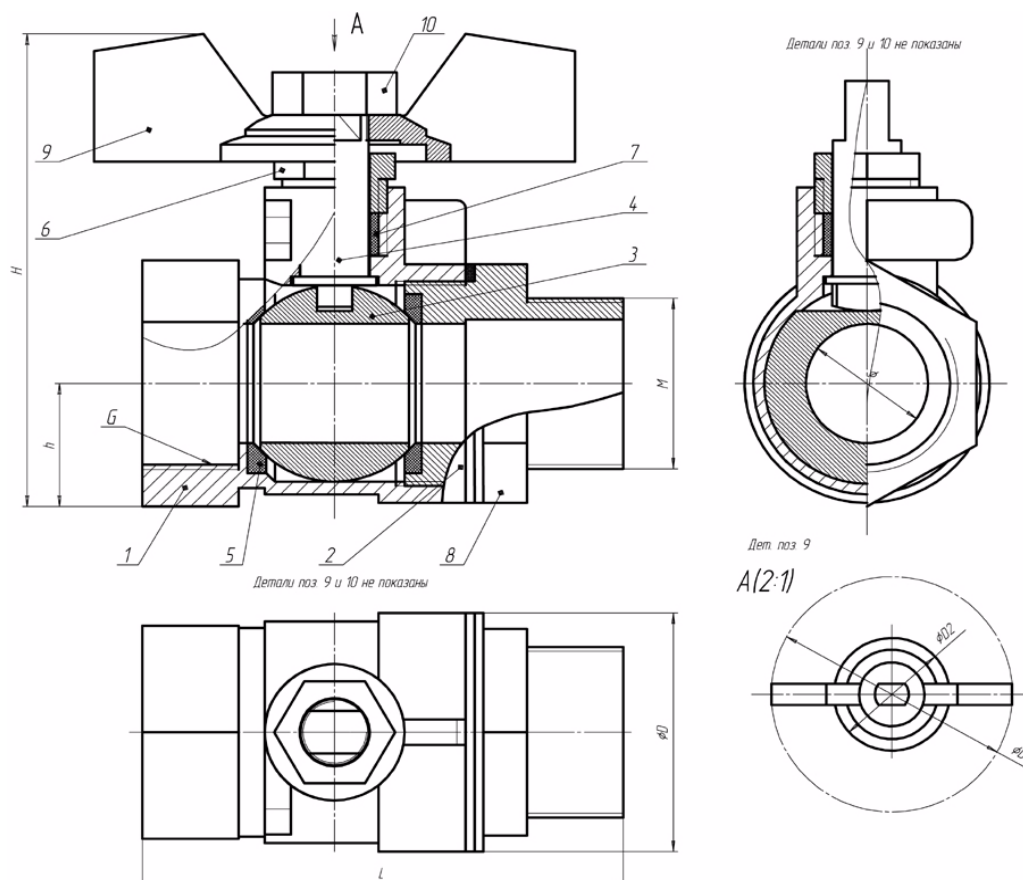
Сборочный чертеж крана проходного сальникового с муфтой и цапкой
